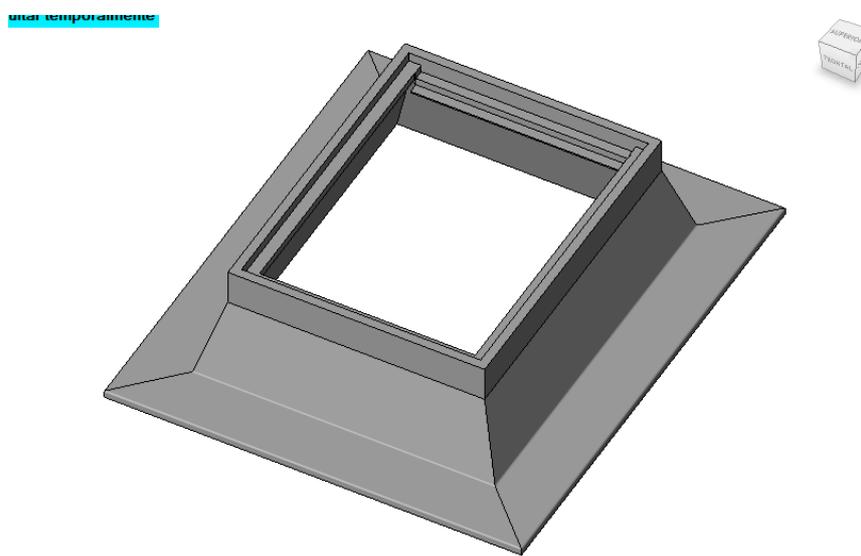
Plantilla para elaboración de la arqueta.
